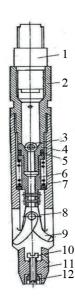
Гидравлический труборез: 1 – бурильная труба; 2 – переходник; 3 – шар; 4 – пята; 5 – резиновое уплотнительное кольцо; 6 – поршень со штоком; 7 – пружина; 8 – ось резцов; 9 – резцы; 10 – болт; 11 – корпус; 12 – гайка
